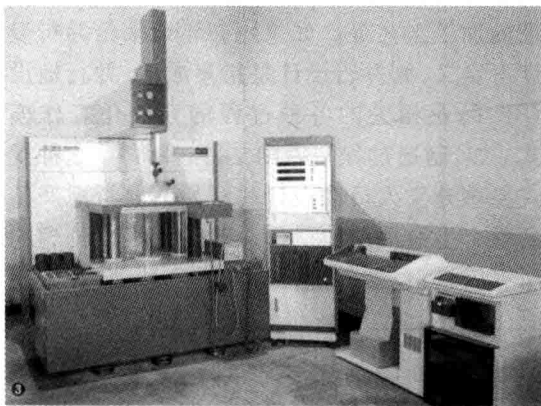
三坐标仪——从模型或实物获得数控加工程序,再通过数控程序的几何数据生成零件图纸
